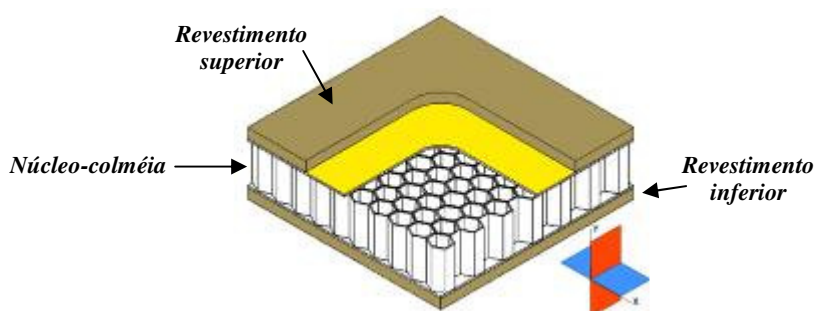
Esquemático dos planos normais (em azul) e transversais (em vermelho) de inspeção por RMN do painel-sanduíche.
